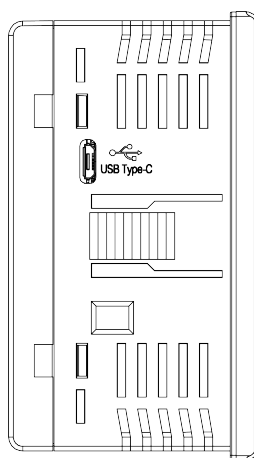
Расположение разъема USB для корпуса Щ1
